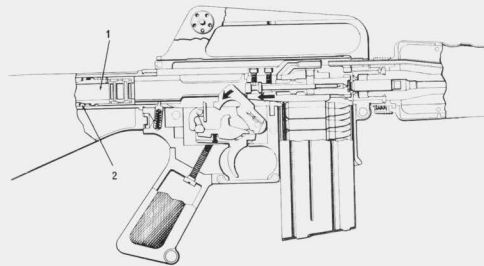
Spannen, Ausziehen: 1 = Rückstoßeinrichtung (Puffer), 2 = Schließfeder
